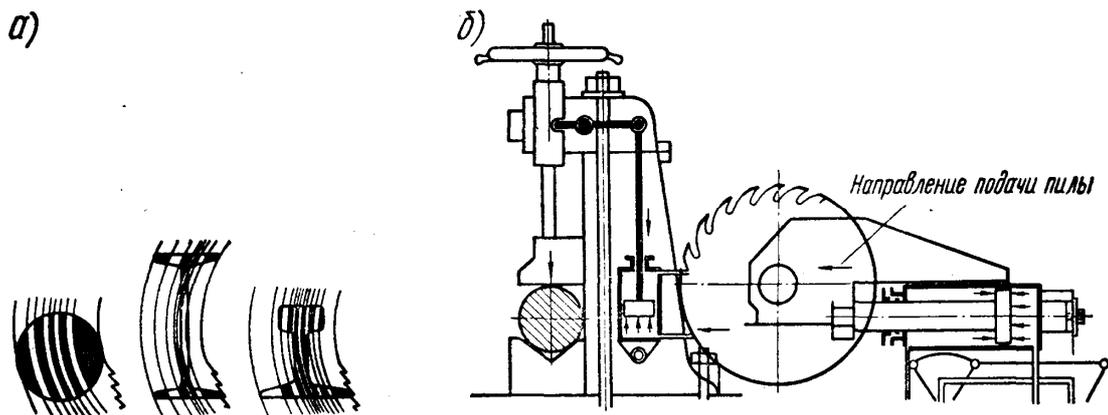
Схема обработки на фрезерно-отрезном станке
